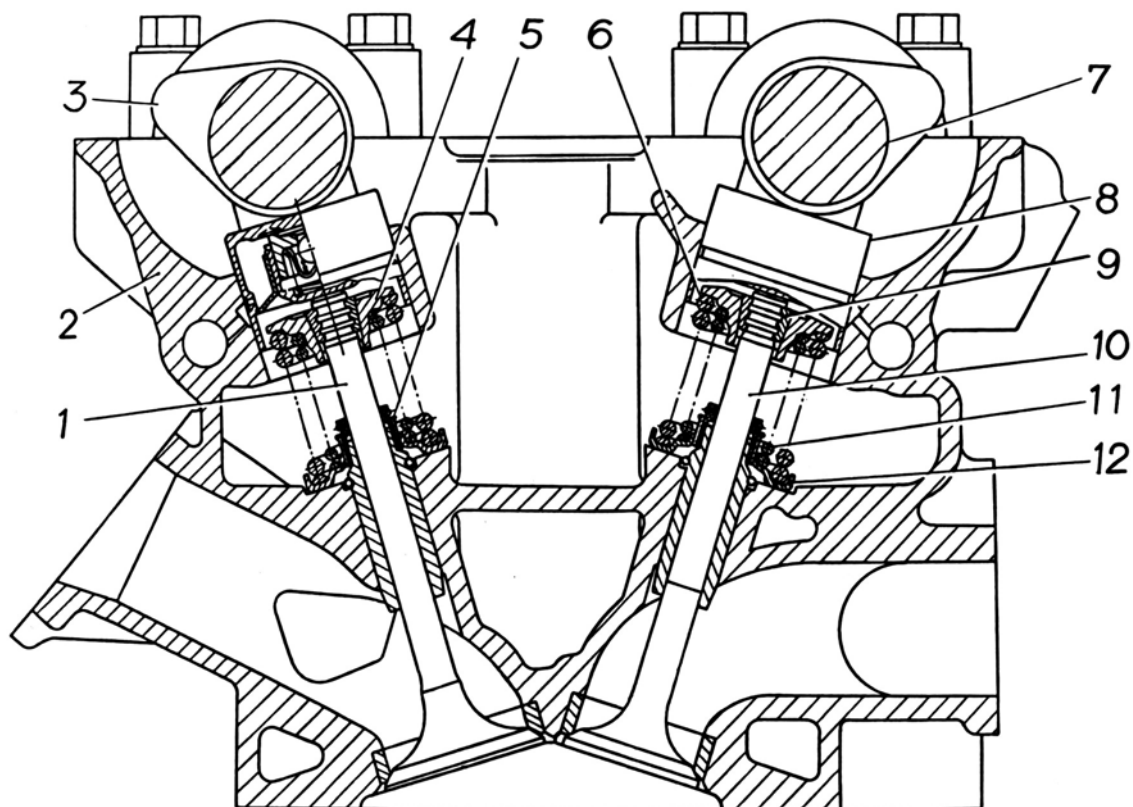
Привод клапанов: 1 - впускной клапан; 2 - головка цилиндров; 3 - распределительный вал впускных клапанов; 4 - тарелка пружин клапана; 5 - маслоотражательный колпачок; 6 - наружная пружина клапана; 7 - распределительный вал выпускных клапанов; 8 - гидротолкатель; 9 - сухарь клапана; 10 - выпускной клапан; 11 - внутренняя пружина клапана; 12 - опорная шайба пружин клапана
